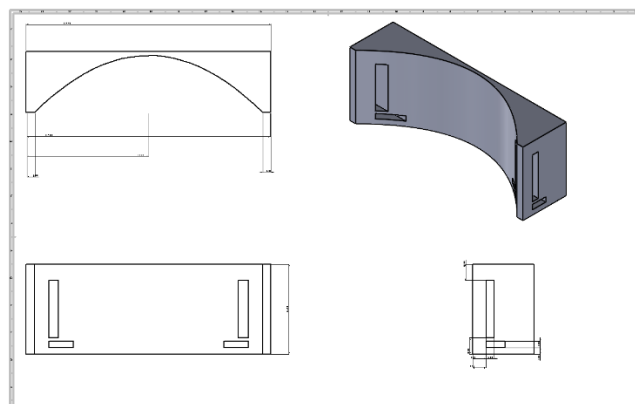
Perspectiva isométrica y vistas diédricas de la pieza 1.
